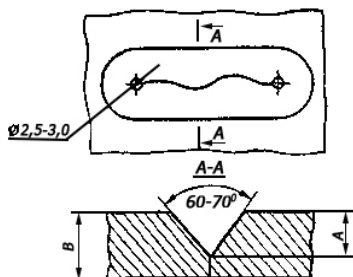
Обробка тріщини під зарівнювання епоксидною композицією
